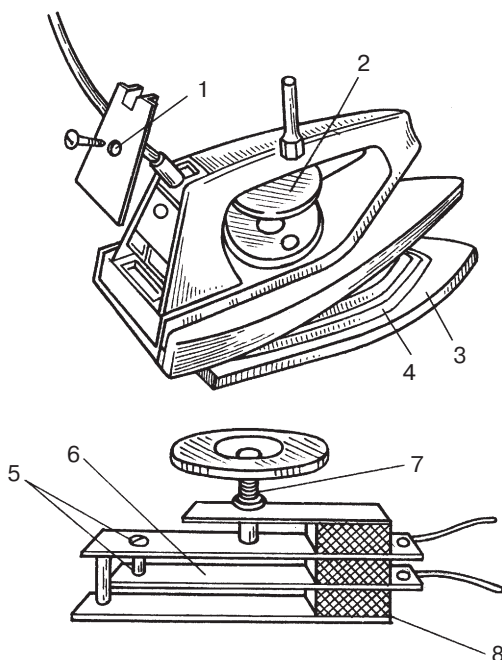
Ремонт утюга с терморегулятором: 1 — задняя крышка; 2 — циферблат; 3 — подошва; 4 — тэн; 5 — контакты; 6 — отжимной лепесток; 7 — регулировочный винт; 8 — биметаллическая пластинка
